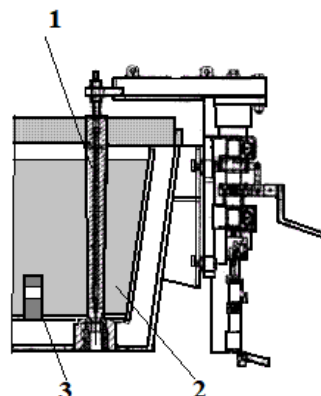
Расположение оборудования в крайней разливочной камере промежуточного ковша:
